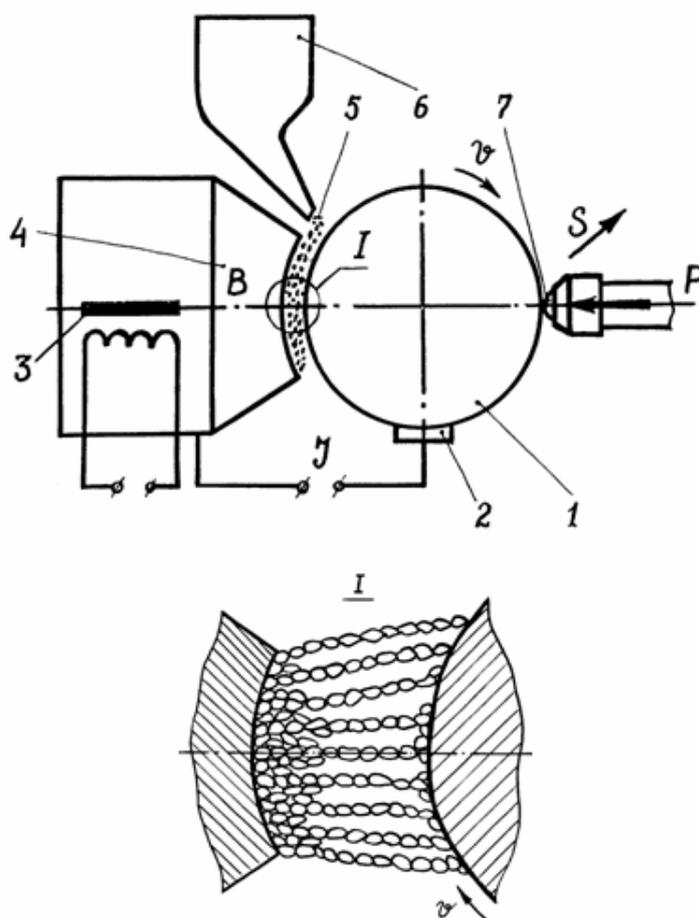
Электромагнитная наплавка с поверхностным пластическим деформированием:
